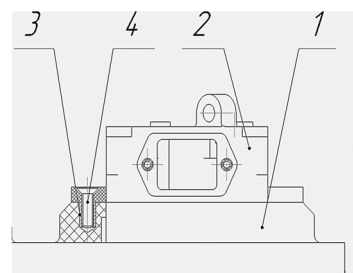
Соединение «Крышка-корпус разъема»:
